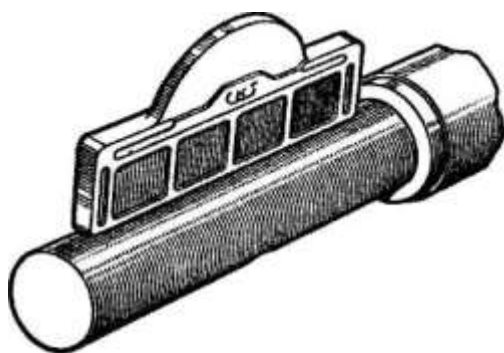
Образец шероховатости при визуальном контроле вала
